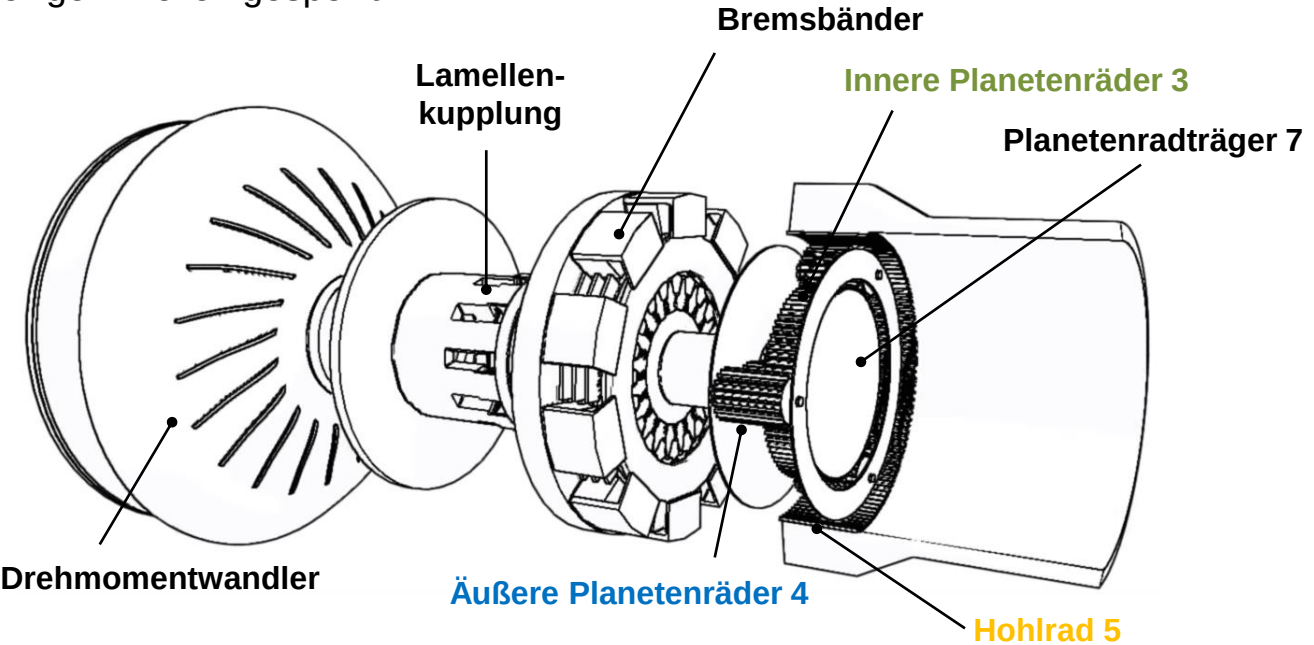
Aufbau eines 4-Gang Automatikgetriebes mit Ravigneaux-Satz [7]
